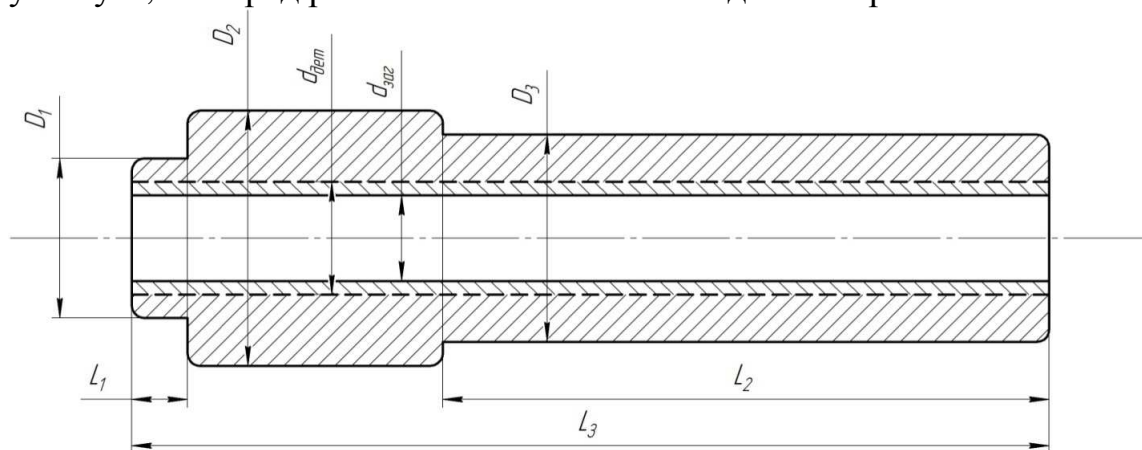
Вид группового чертежа штампованой или горячекатаной трубной заготовки цилиндра: $d_{заг}$ – диаметр глубокого отверстия заготовки; $d_{дем}$ – диаметр глубокого отверстия детали; D_1 – диаметр наиболее короткой части; D_2 – наибольший диаметр заготовки; D_3 – диаметр наиболее длинной части; L_1 – длина наиболее короткой по размеру части; L_2 – длина средней по размеру части; L_3 – общая длина заготовки цилиндра
